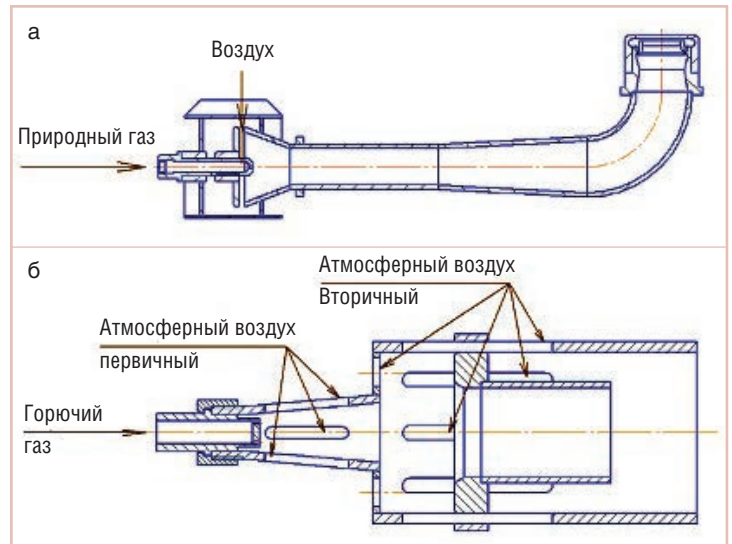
Газовоздушные горелки для разогрева 5-тонных сталеразливочных ковшей шиберного типа: а — ГВТ-15; б — ГН 53/3,9 М
